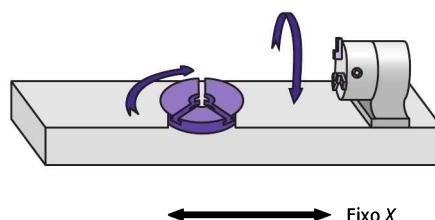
Eixos rotativos programáveis podem ser adicionados aos acessórios ou integrados a partes da máquina.
